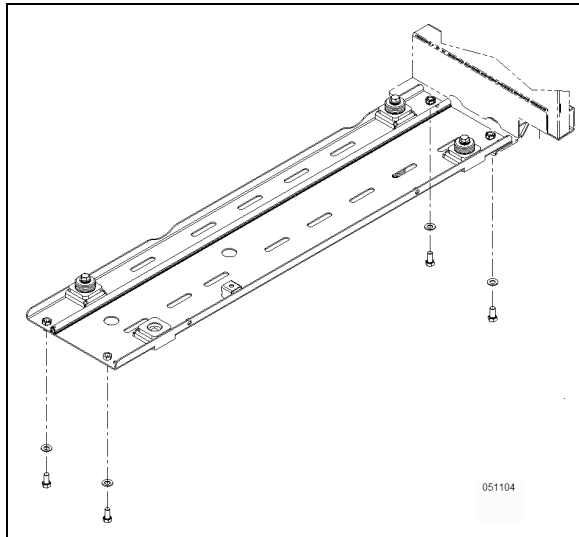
TORNILLOS DE MONTAJE DEL SOPORTE INFERIOR
